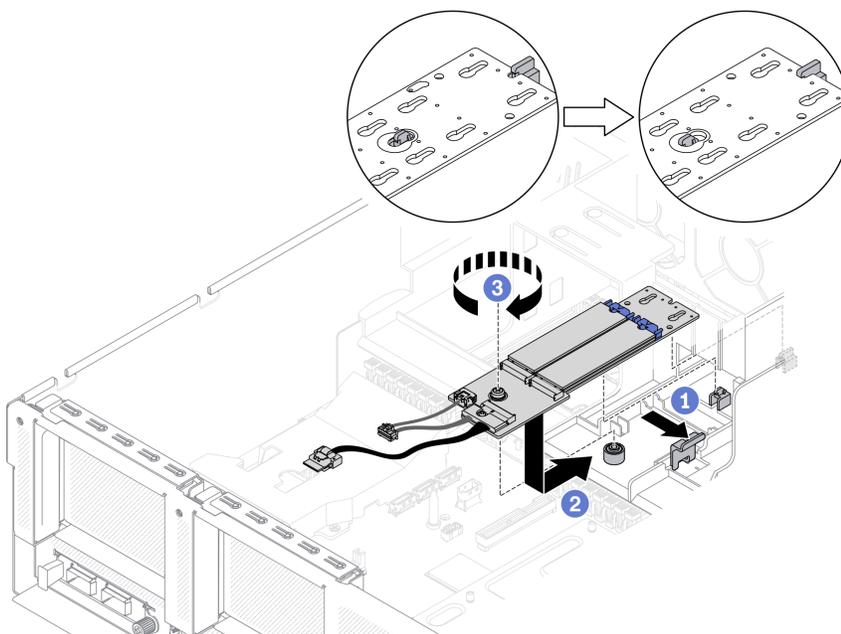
Installation du fond de panier M.2 sur la grille d'aération
